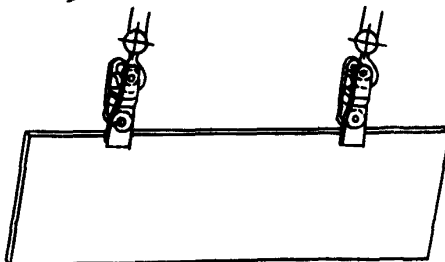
Кантовка крупногабаритных листовых деталей серьгами с приваркой строповочных проушин
